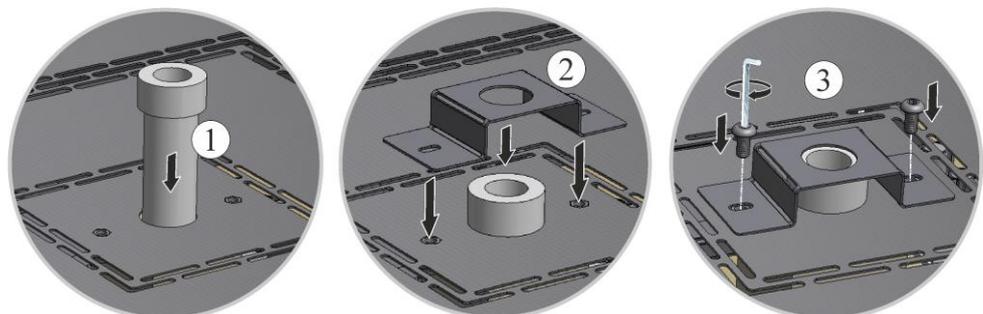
Montagem do tubo do ar de exaustão (semelhante à figura)
